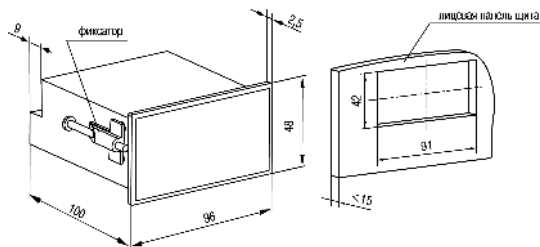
Габаритные размеры корпуса Щ2
